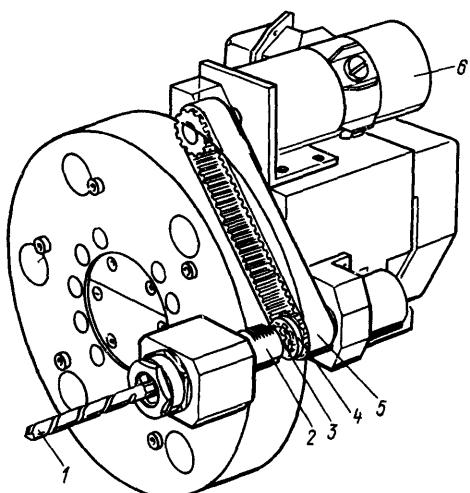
Револьверная головка с приводом 6 для инструмента 1:
